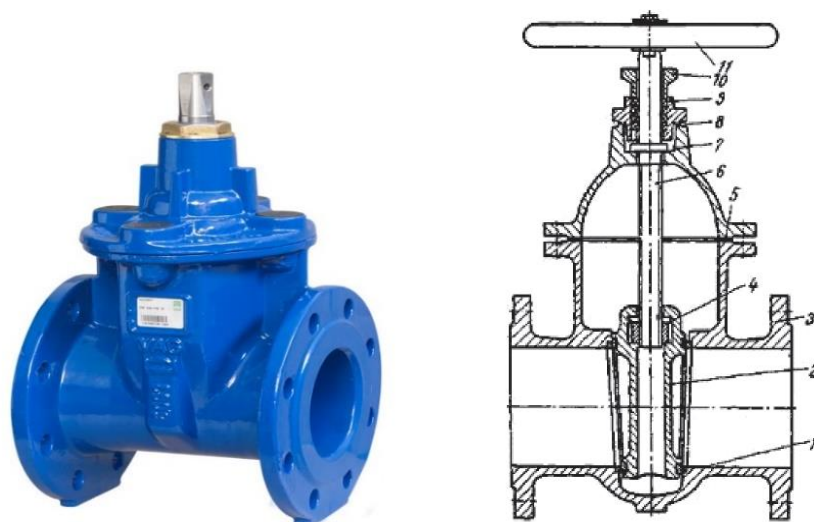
Внешний вид и чертеж клиновой задвижки и ее основные части:
